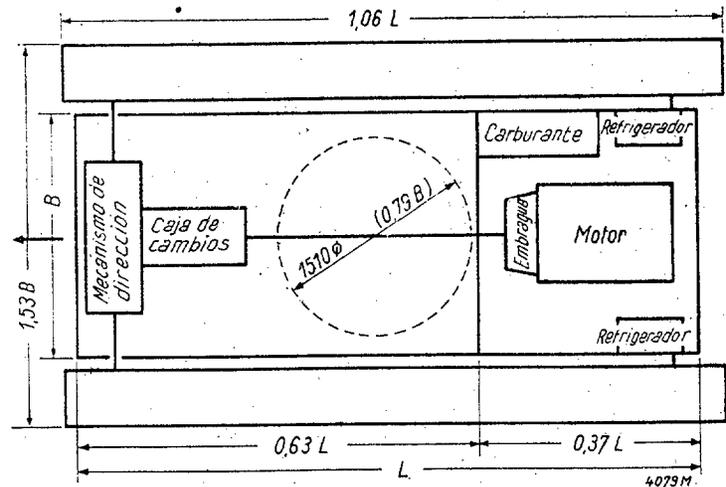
Esquema constructivo de un tanque con tracción delantera.
